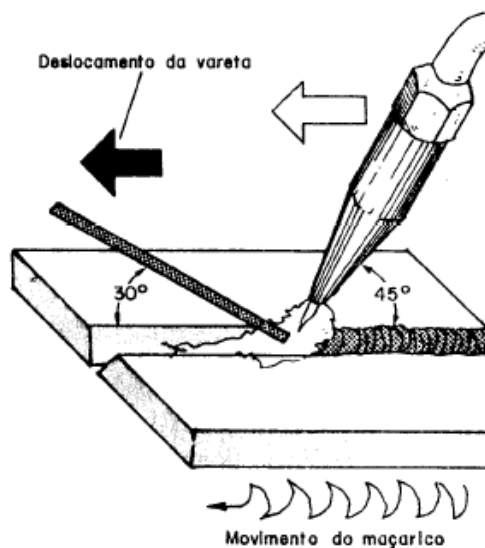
Representação esquemática da soldadura oxiacetilénica
